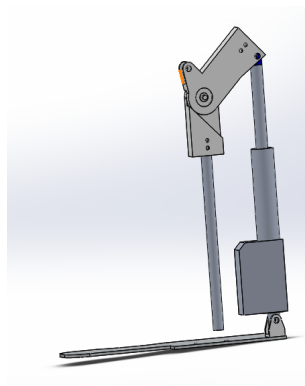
Diseño CAD del eslabon de rodilla del exoesqueleto
